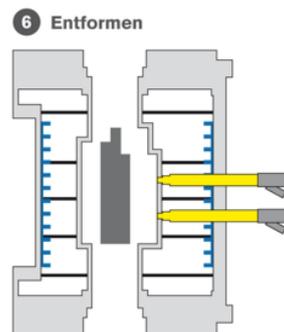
Pneumatische gesteuertes Auswerfen des Formteils
